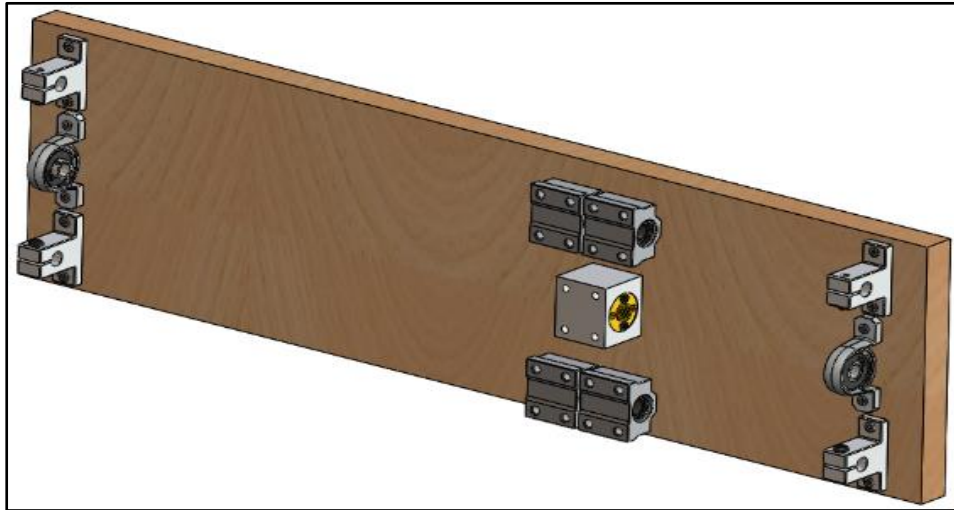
Posicionamiento del bloque de aluminio y de los rodamientos lineales con soporte SC8UU en la base eje Y
